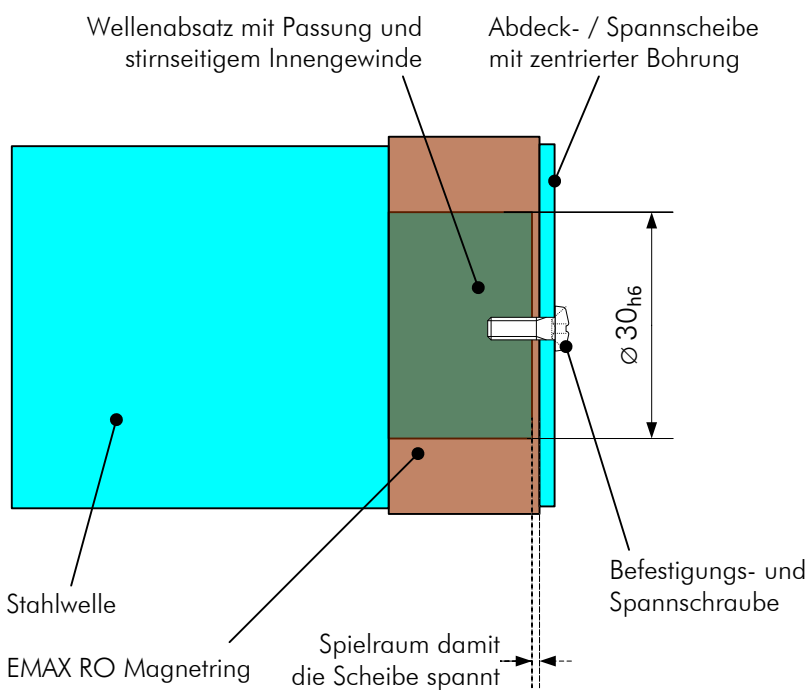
Magnetring: Montagebeispiel Schraubmontage
